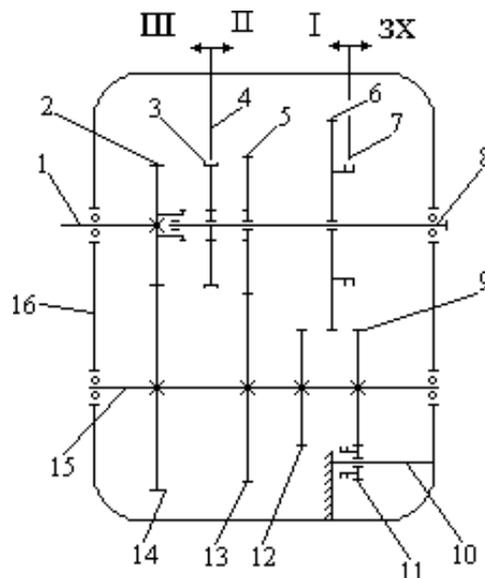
Кінематична схема тривалової триступеневої коробки передач
